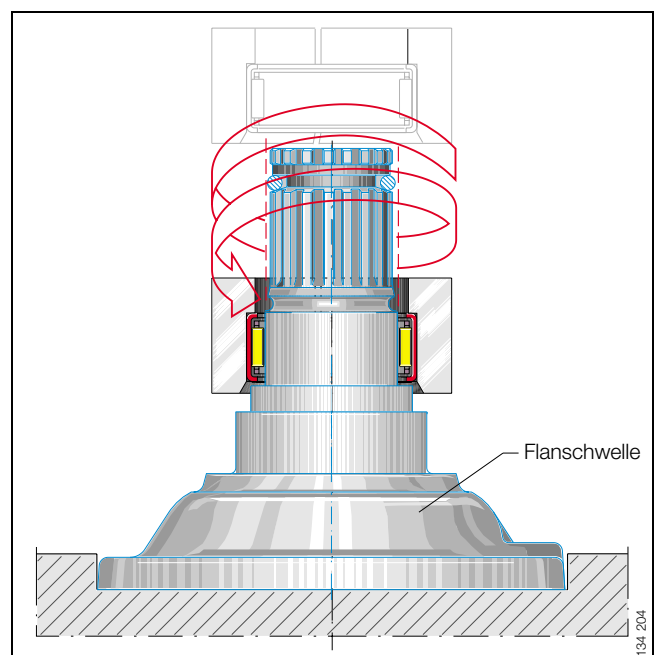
· Lager mit Drehbewegung auf der Welle montieren
